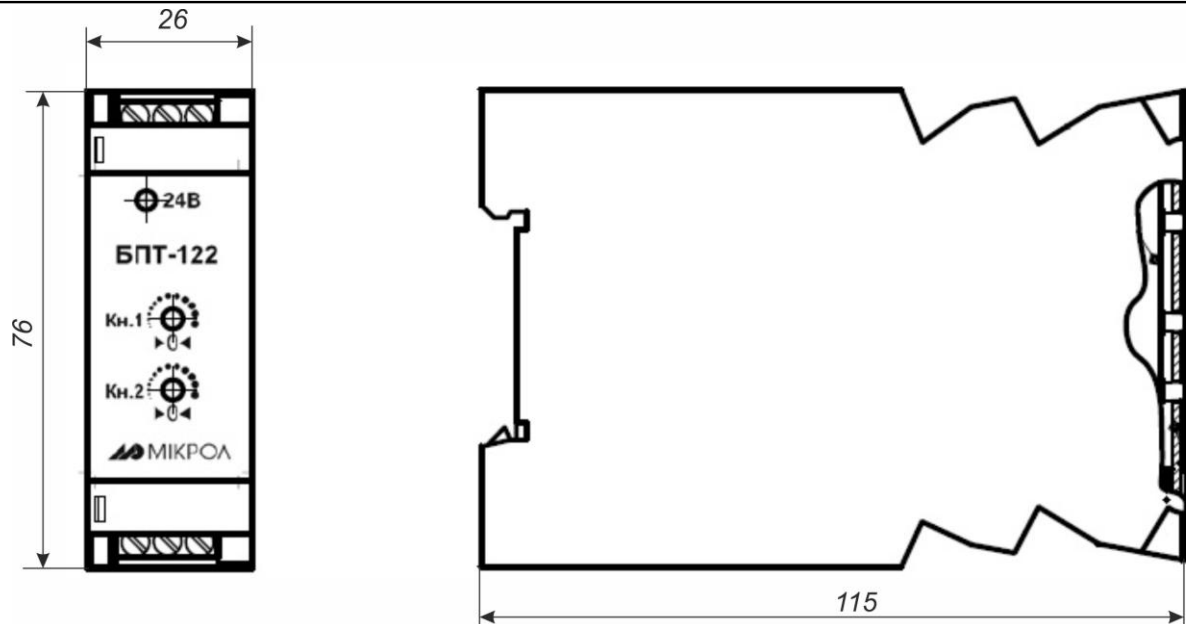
Зовнішній вигляд і габаритні розміри блоку БПГ-122
